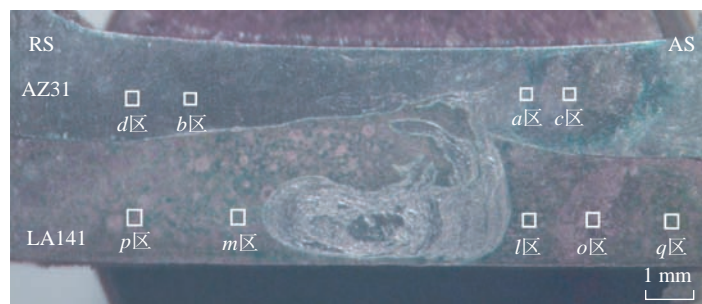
1800 r/min-120 mm/min 参数下搭接接头横截面宏观形貌
